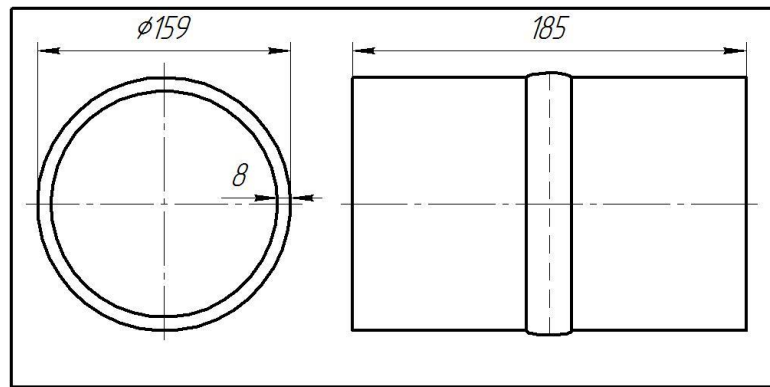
Стыковой сварной образец из труб $\phi 159$.
